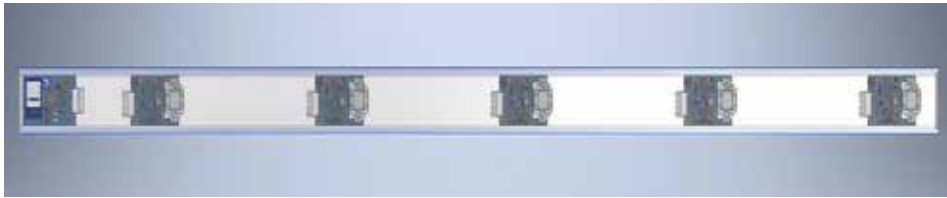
Загальний очікуваний вигляд корпусу світильника (фронтальний вид)
